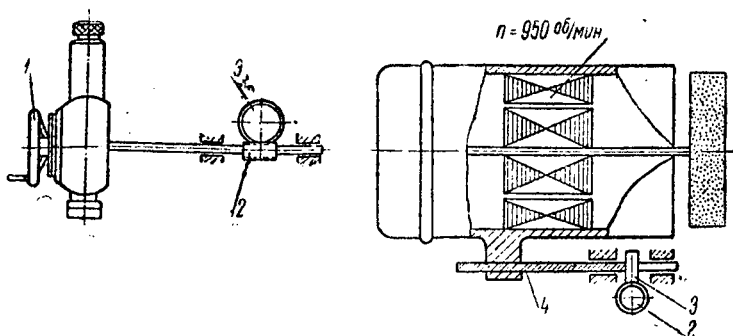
Механизм ручной подачи шлифовального круга на станке 373-С МСЗ
